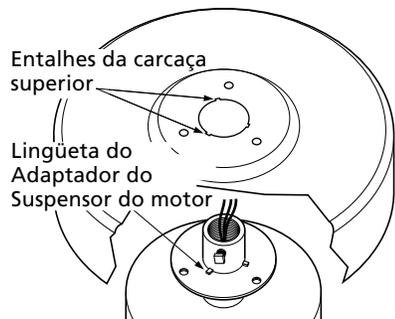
Linguetas do adaptador do suspensor do motor e entalhes da carcaça superior
